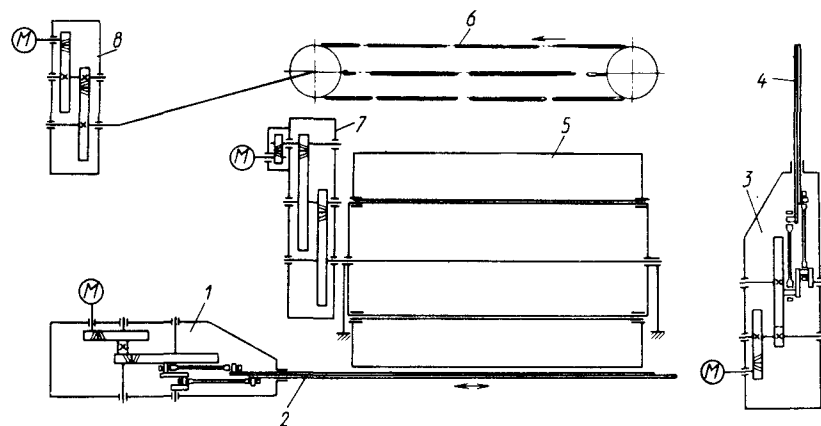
Кинематическая схема кусторезного оборудования:
